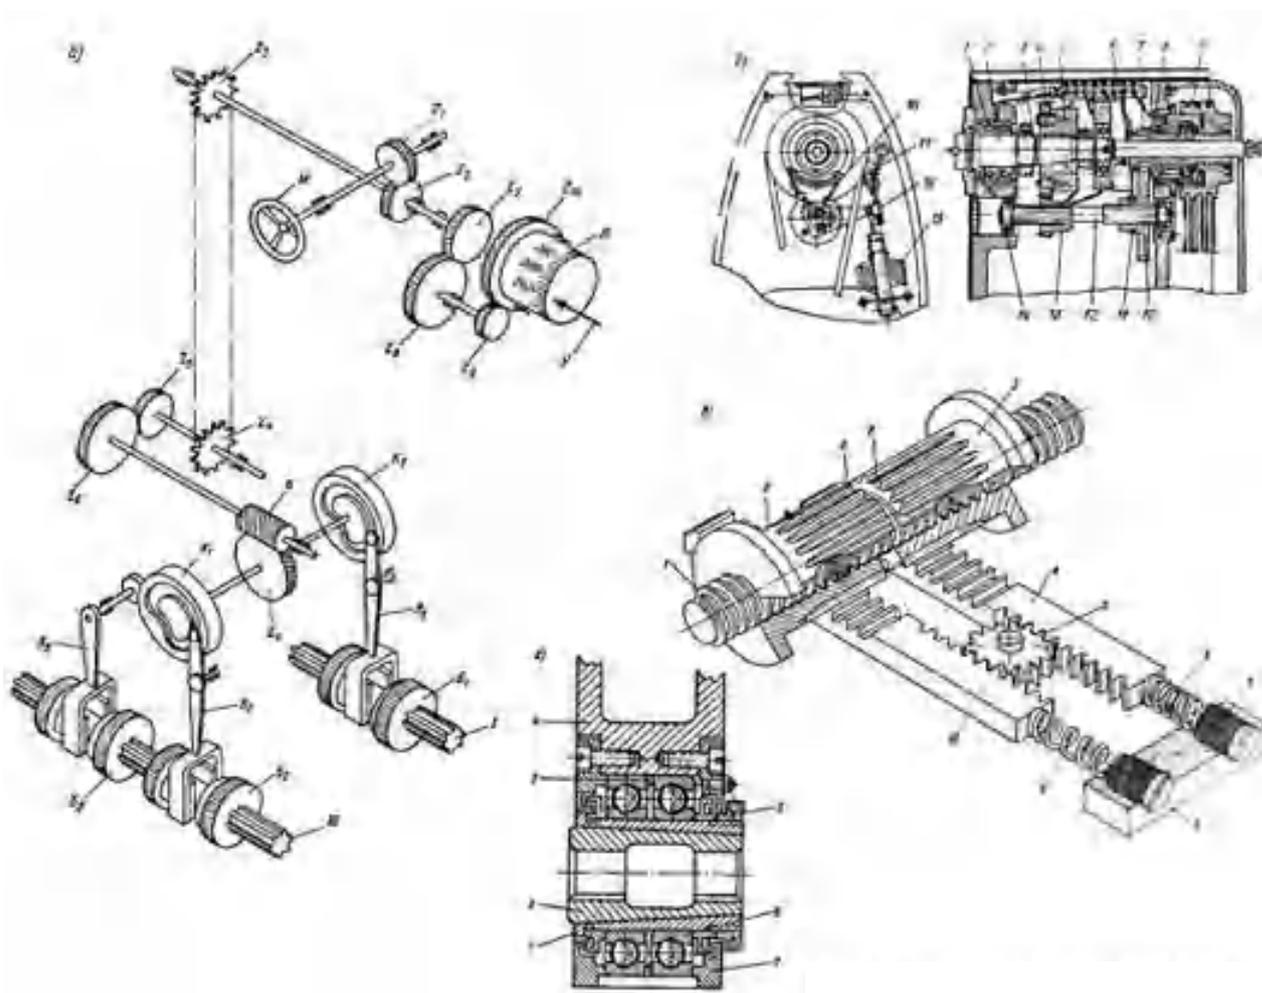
Узлы консольно-фрезерного станка 6Н81Г
